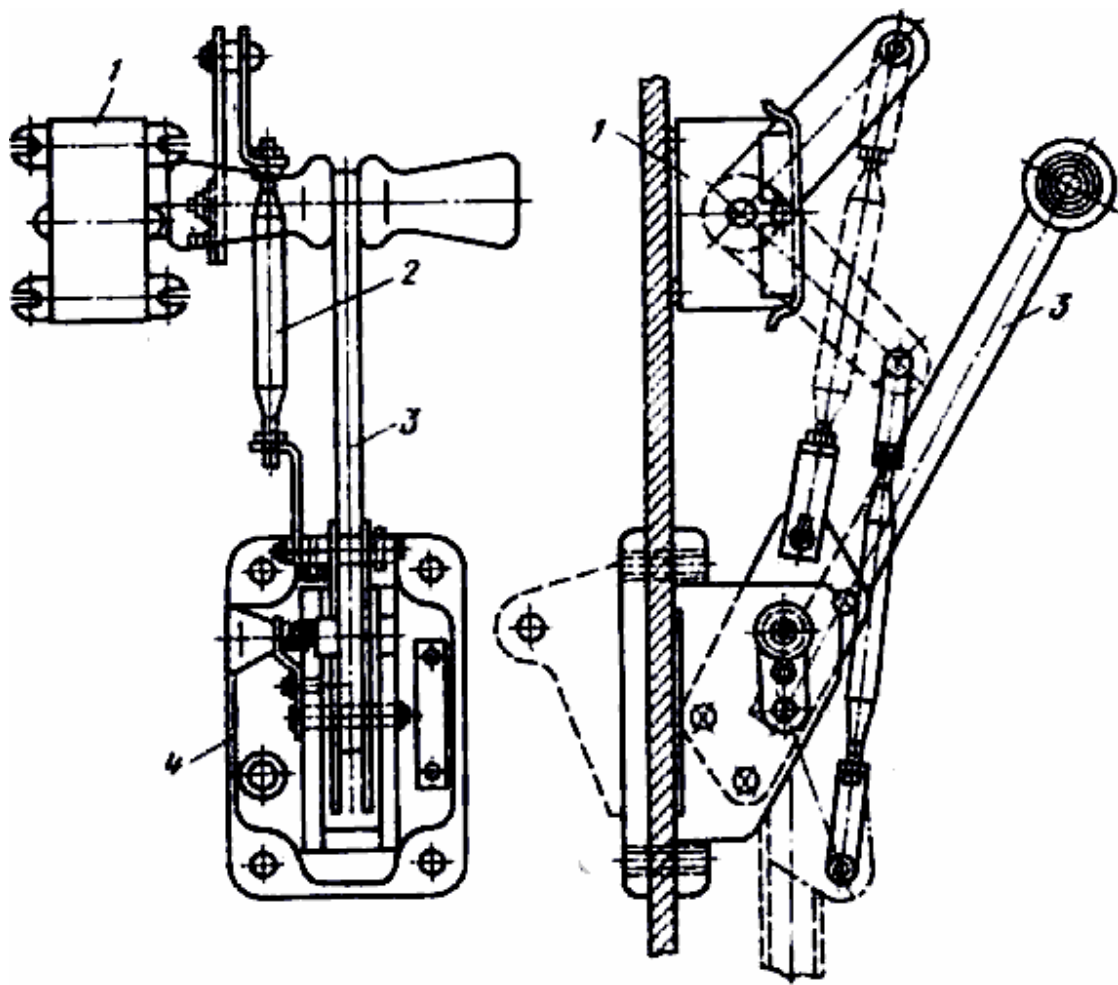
Установка вспомогательных контактов к рычажному приводу разъединителя
